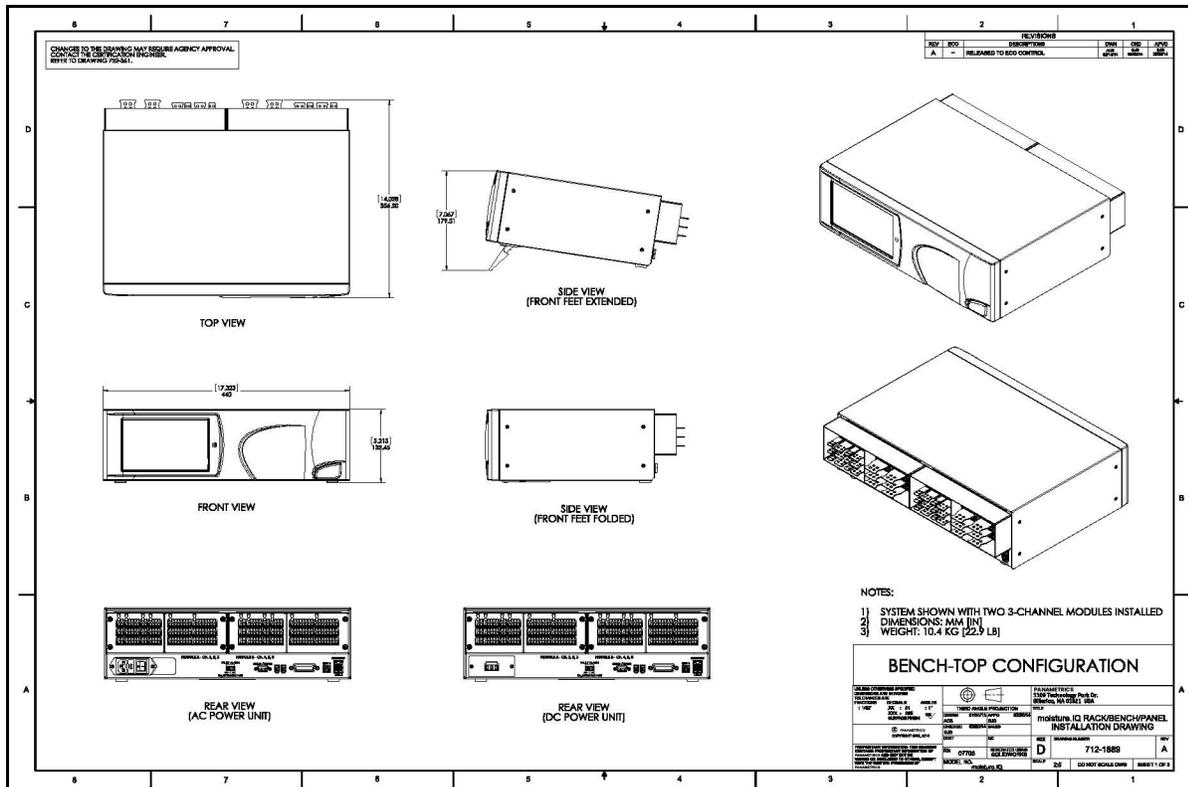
Configuración de sobremesa (Plano 712-1889_revA, SH 1 de 3)
